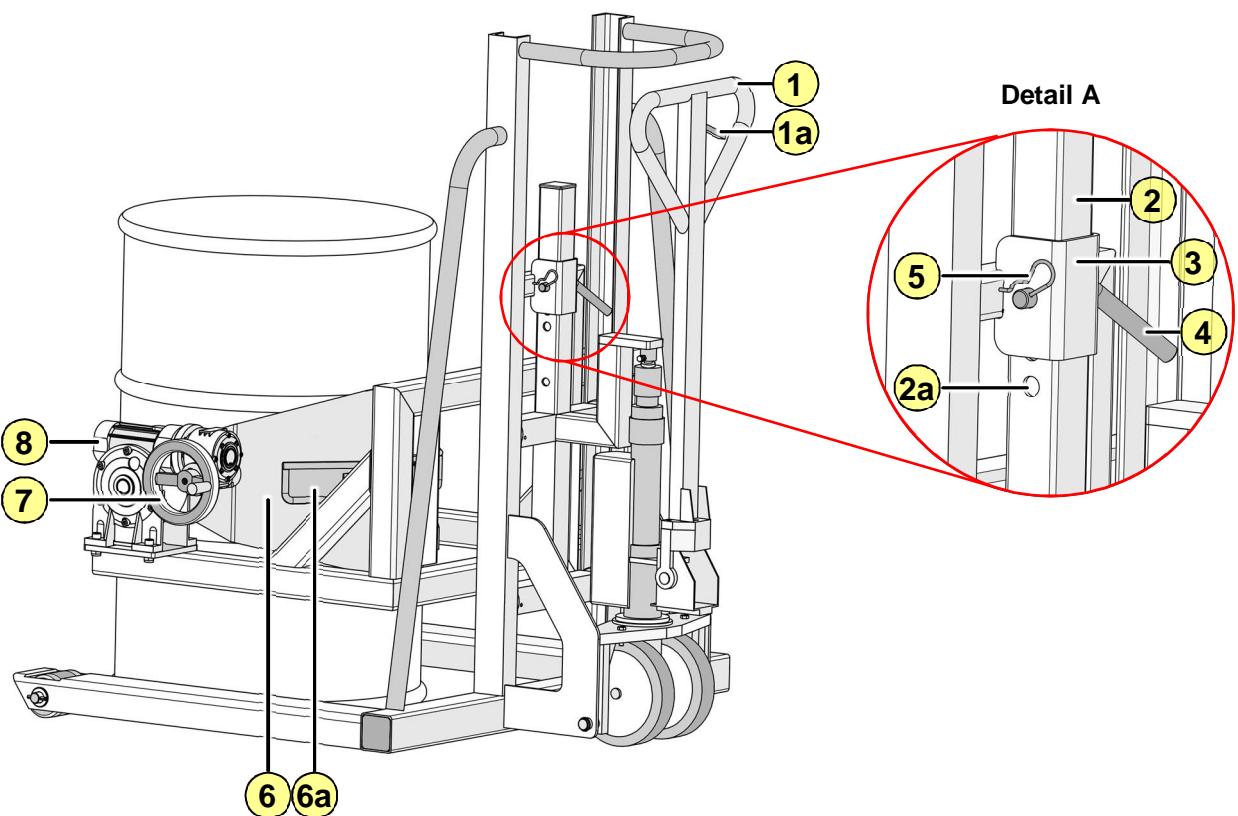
Baugruppen Fassheberoller, Typ FHR 600 F
